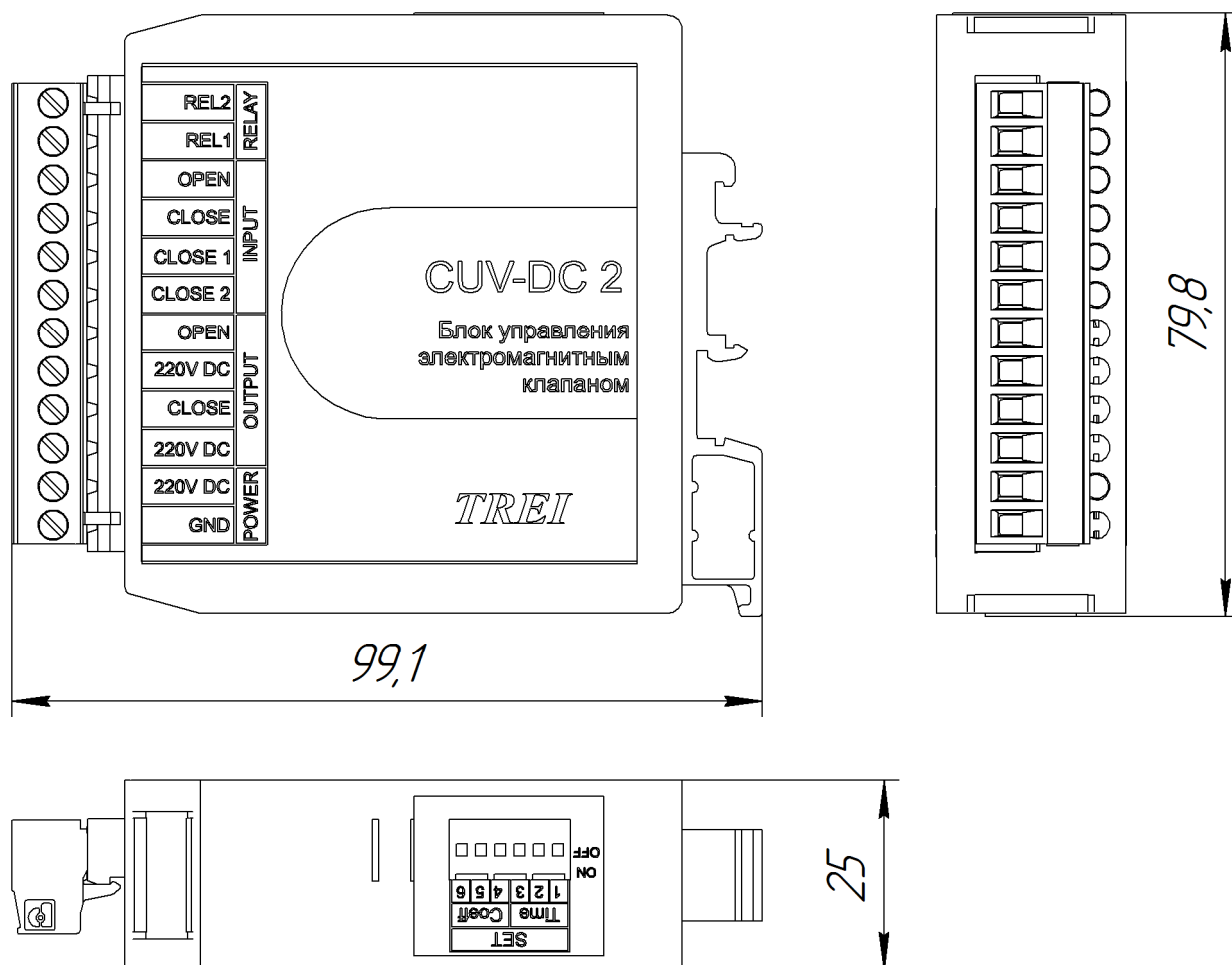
Чертеж общего вида CUV-DC 2 с указанием габаритных и присоединительных размеров
